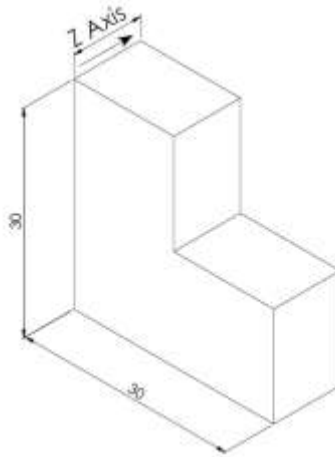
Dimensiones de las muestras y posición del eje Z.
